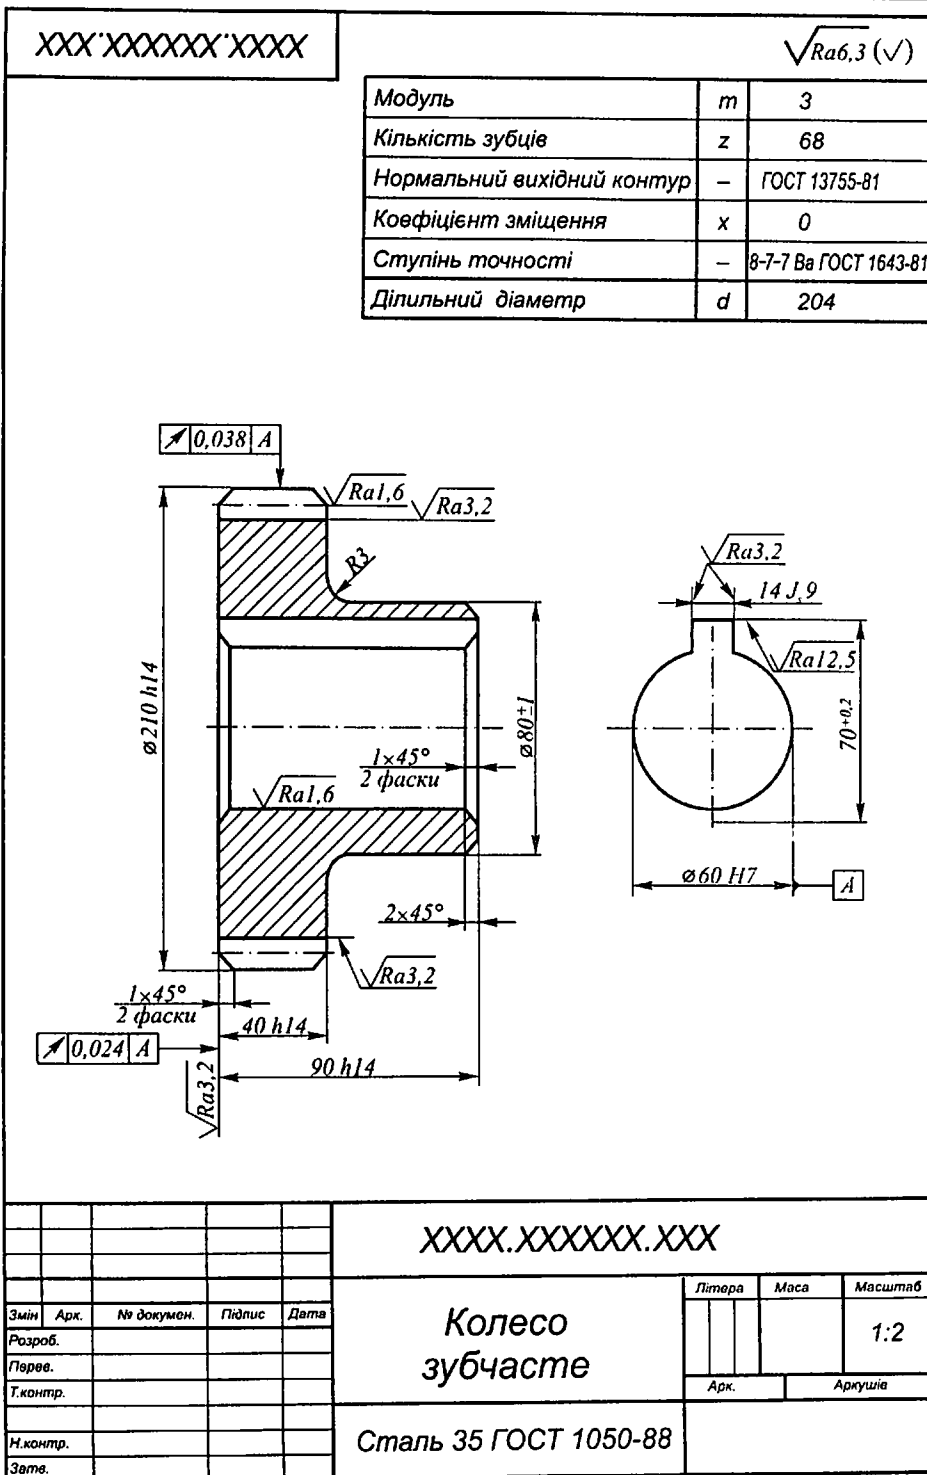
Приклад виконання кресленника циліндричного зубчастого колеса
